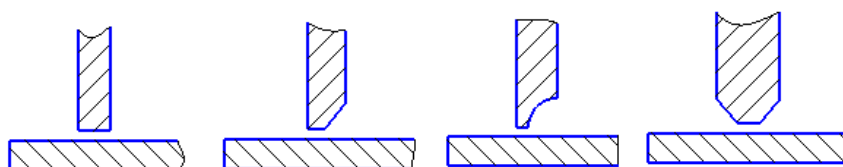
Форма подготовленных кромок под сварку для тавровых соединений [20].
